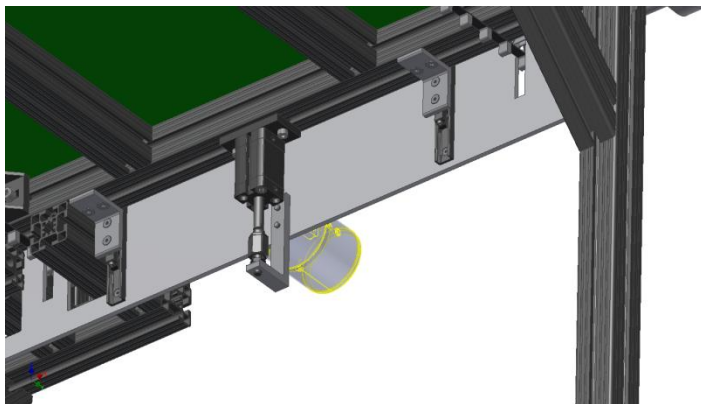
Poslední pozice zásobníku - prizmatické lůžko dole
